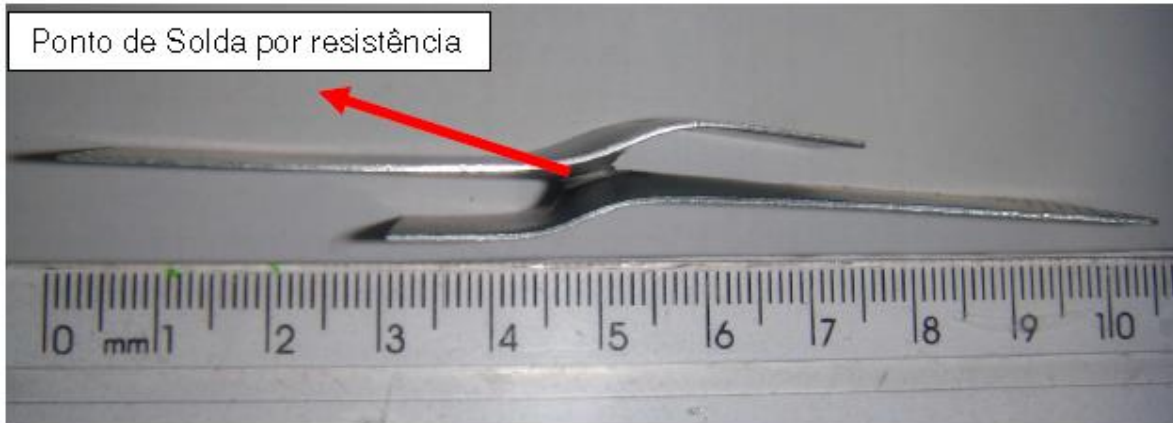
Vista de topo das tensões aplicadas
